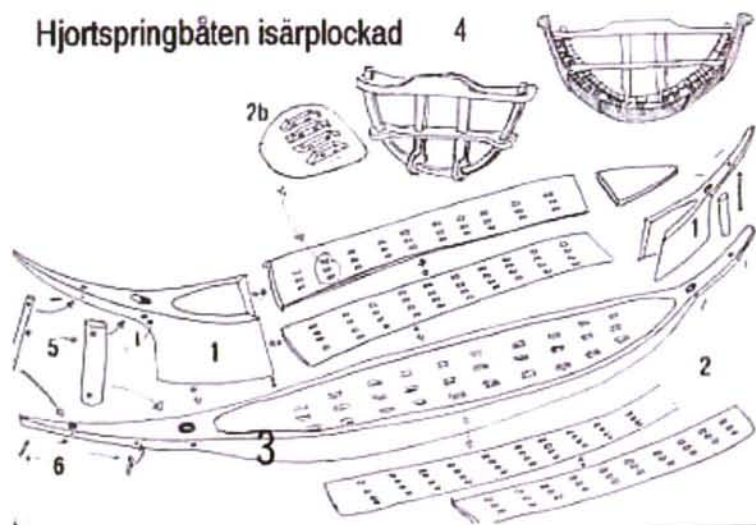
Despiece del bote de Hjortspring. [AXEL: <http>].
